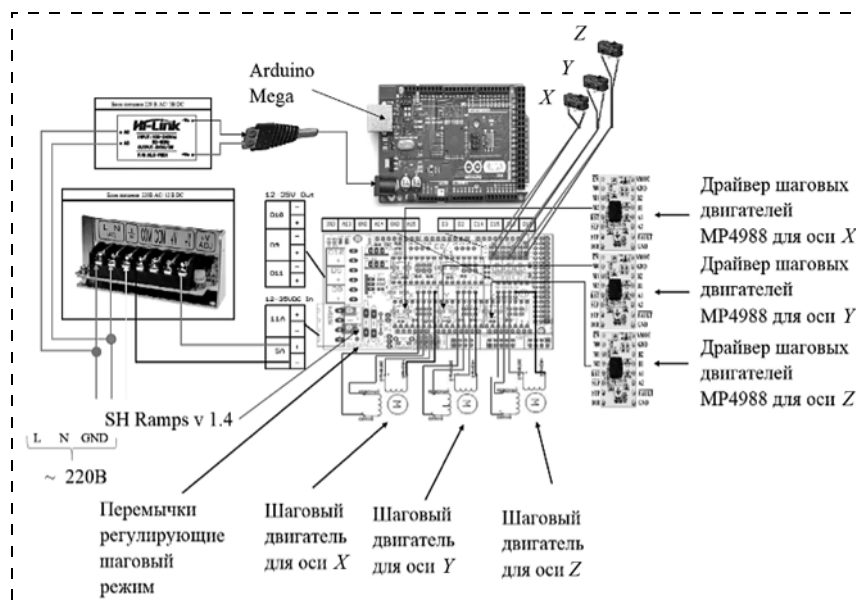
Электрическая схема трехосевого фрезерного станка с ЧПУ
